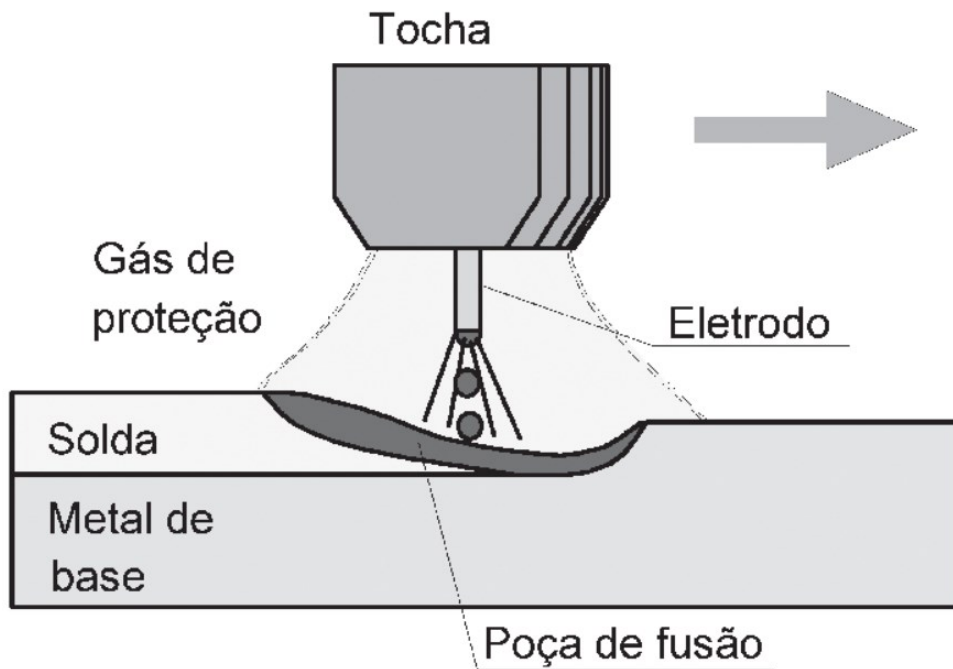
Esquema de soldagem MIG/MAG (MARQUES, 2016).
